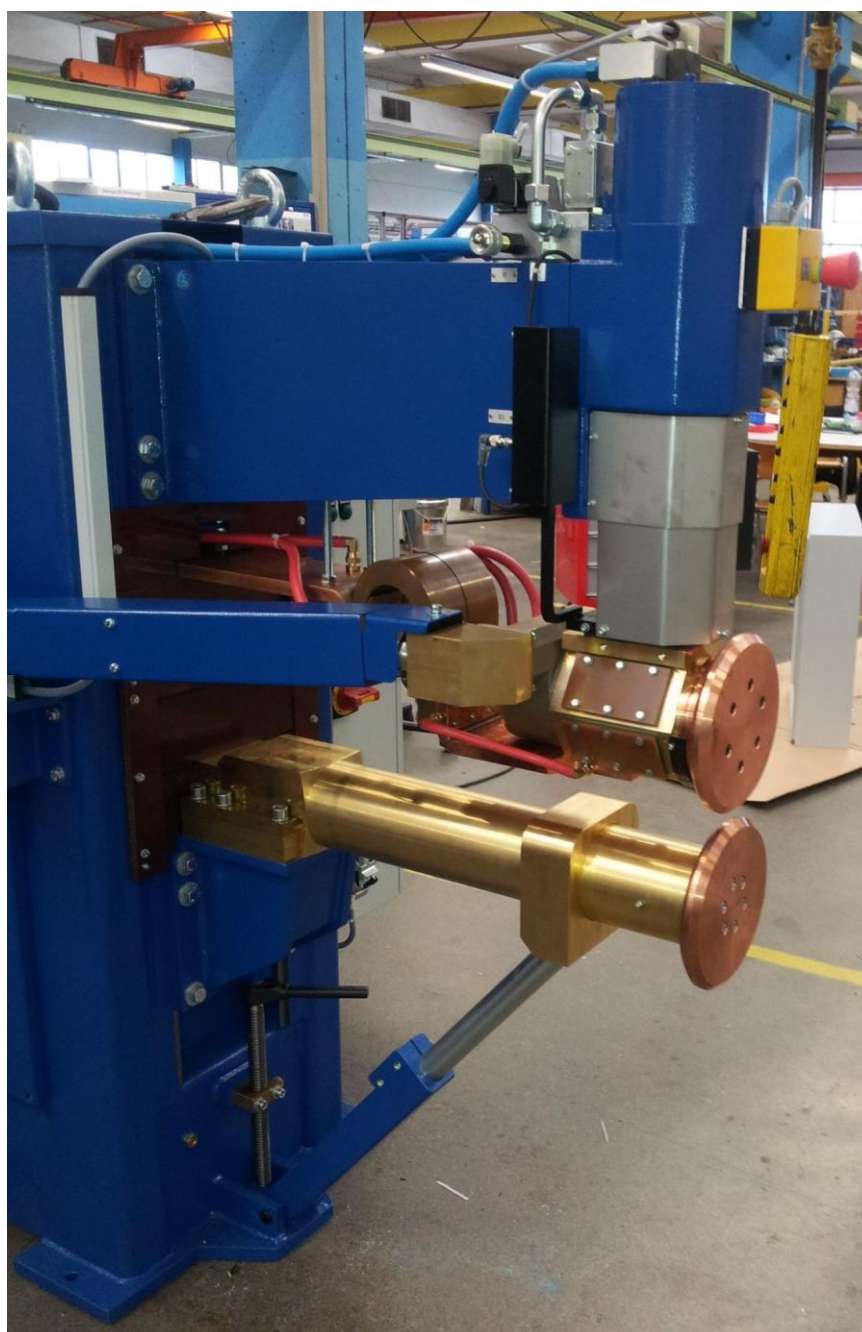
Машина для шовной сварки PMS 44-6
